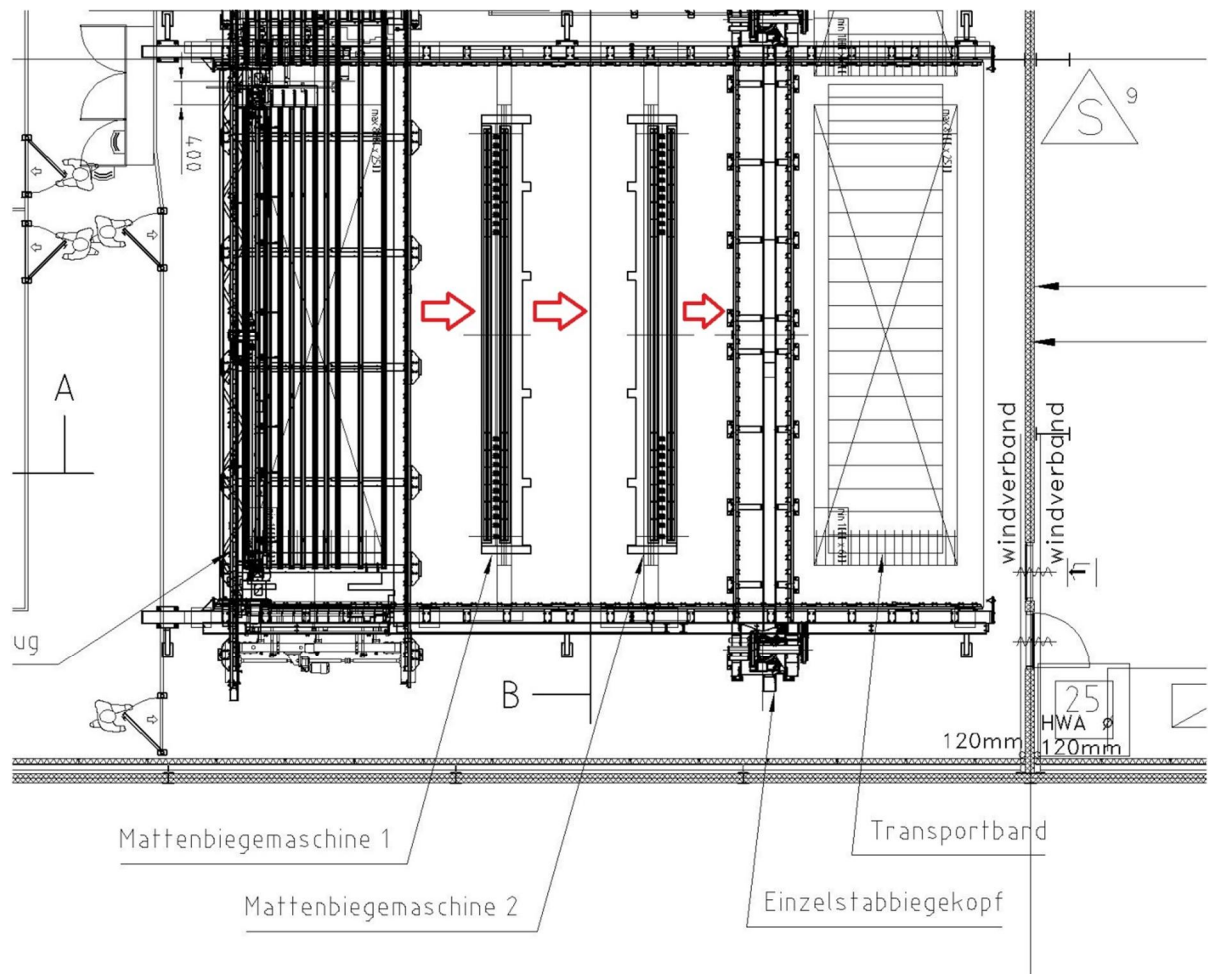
Detail Layout Biegemaschine, rot gekennzeichnet der Weg der Matte zum gebogenen Endprodukt
